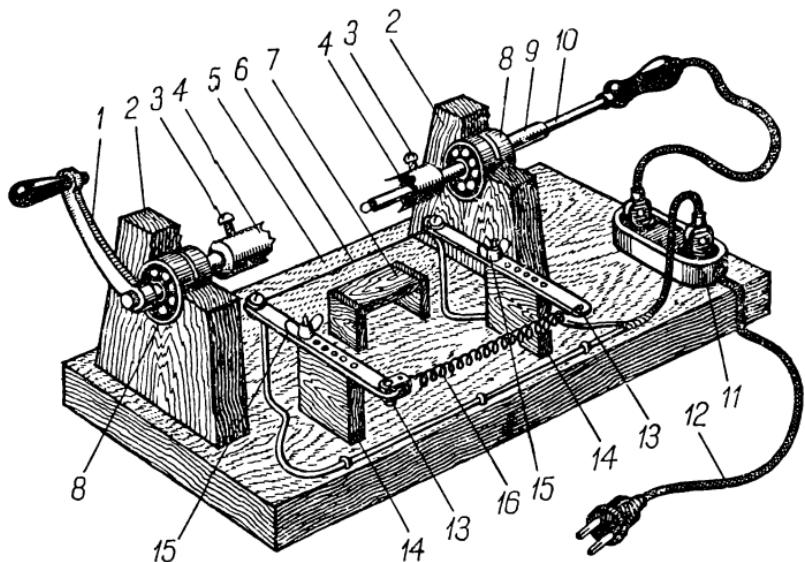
Станок для изготовления корпусов ракетомоделей:
